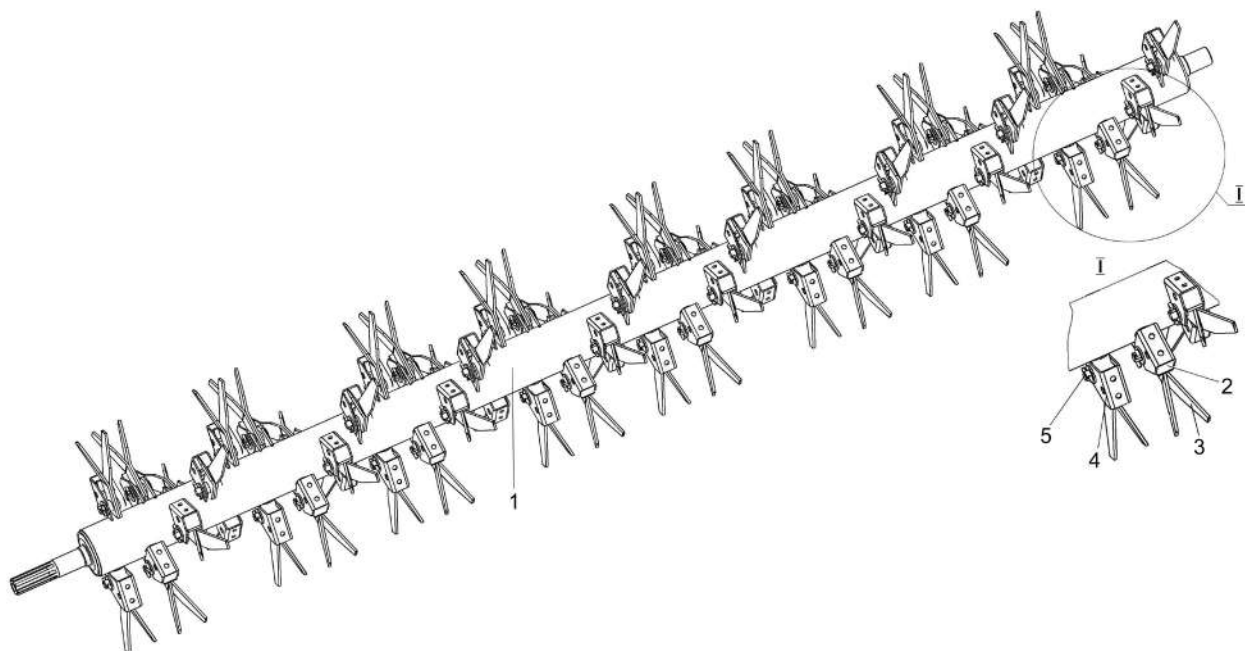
Устройство бильное: 1 – вал; 2 – демпфер; 3 – бич; 4 – корпус;
